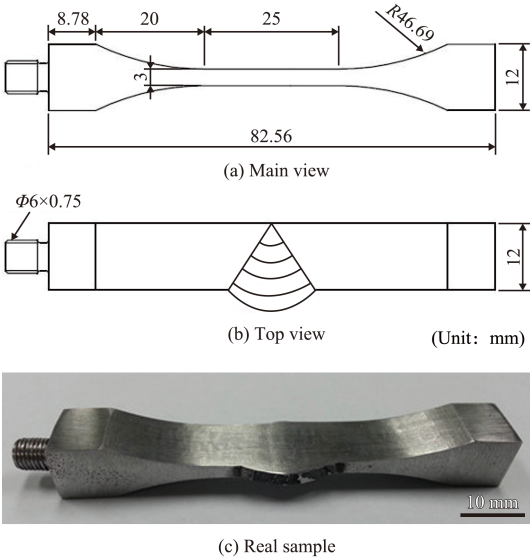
SMA490BW 焊接接头试样形状尺寸及实物
